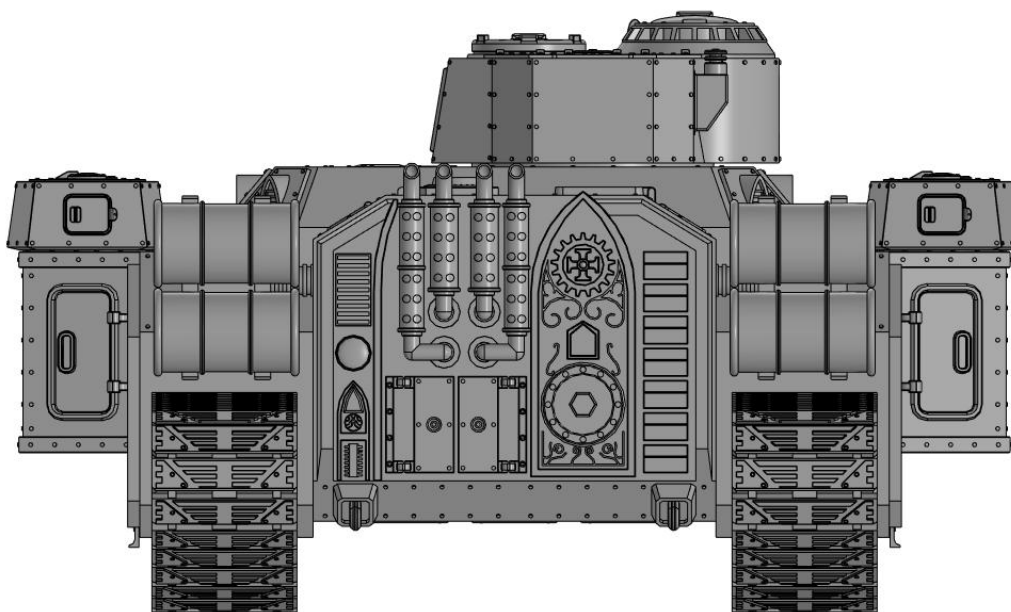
Готовая модель танка «гибельный клинок», вид сзади
